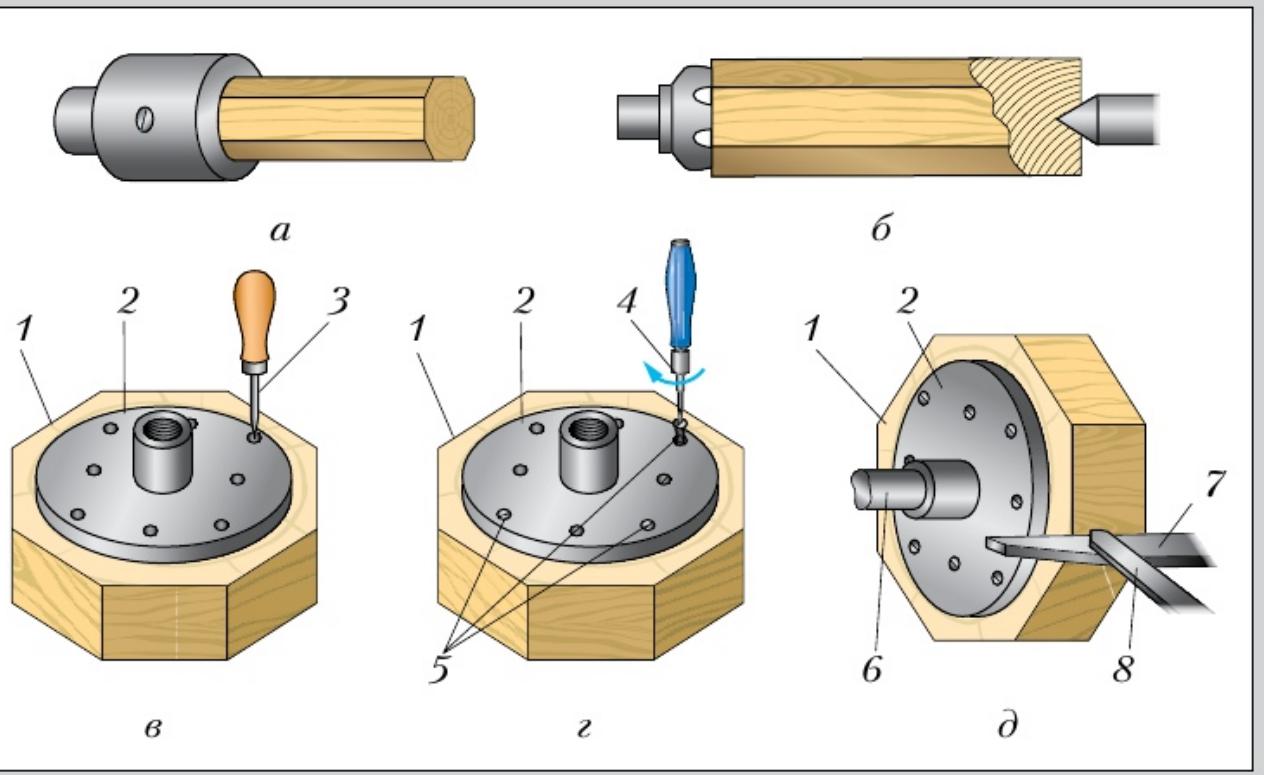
Крепление заготовки: *а* – в патроне винтом; *б* – с помощью трезубца и заднего центра; *в–д* – на планшайбе: 1 – заготовка; 2 – планшайба; 3 – шило; 4 – отвёртка; 5 – шурупы; 6 – шпиндель; 7 – подручник; 8 – режущий инструмент (стамеска)
